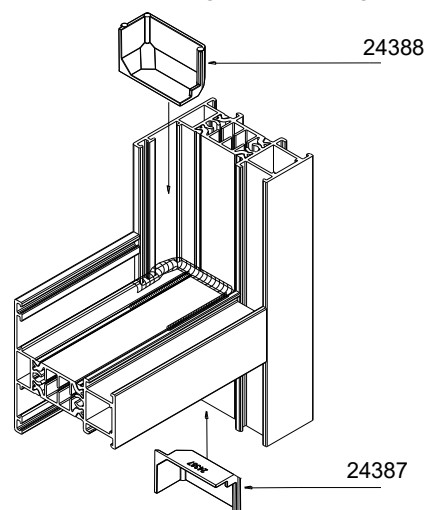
DETAILS ETANCHEITE TRAVERSES/MENEAUX
